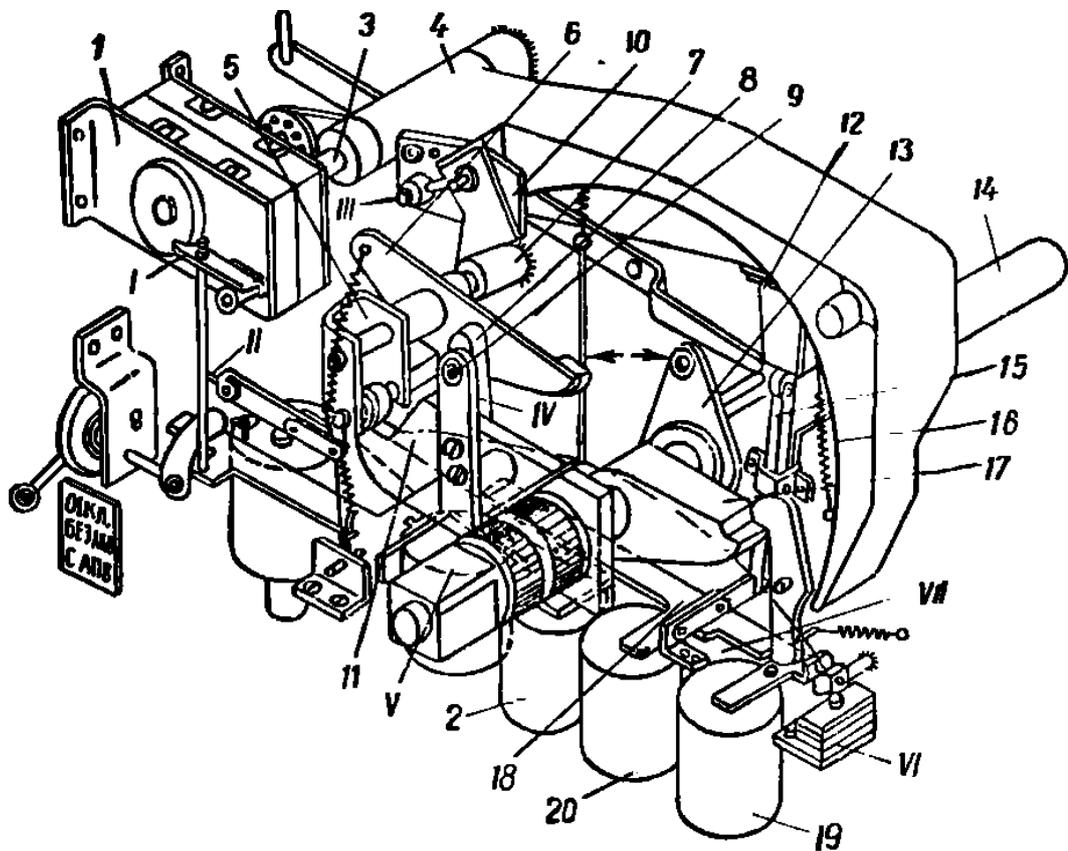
Кинематическая схема пружинного привода типа ППМ-10
